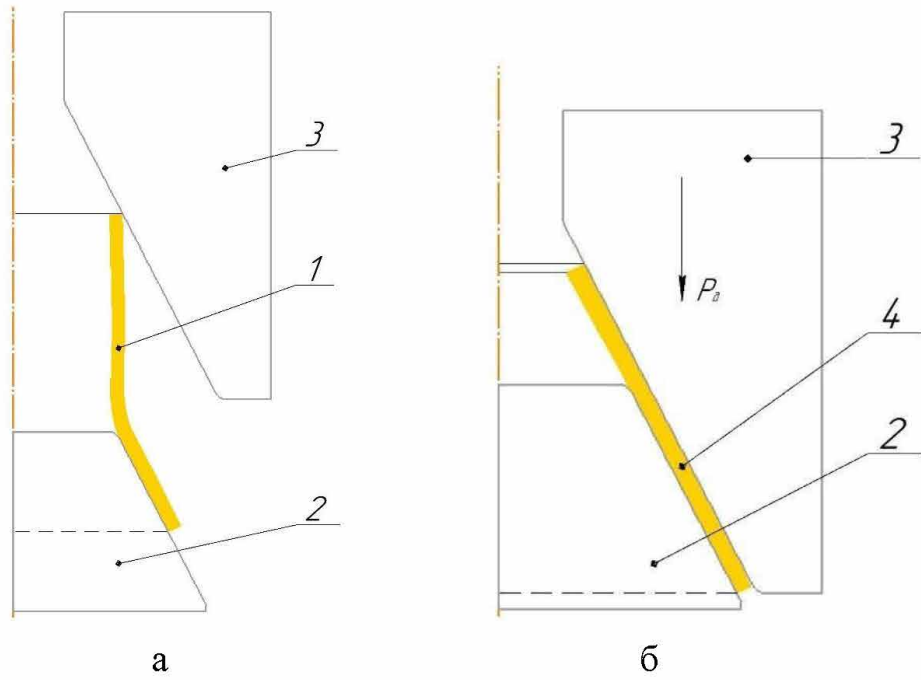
Схема процесу обжиму трубної заготовки:
